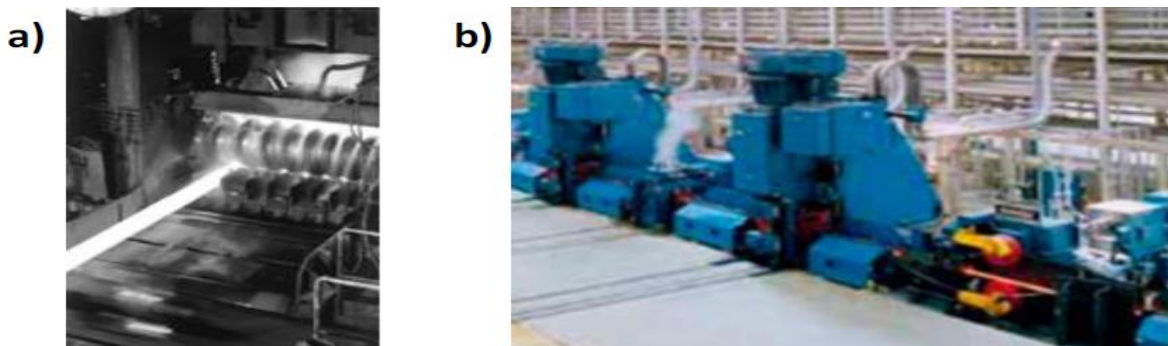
Exemple : (a) de laminoir réversible et (b) de laminoir tandem
